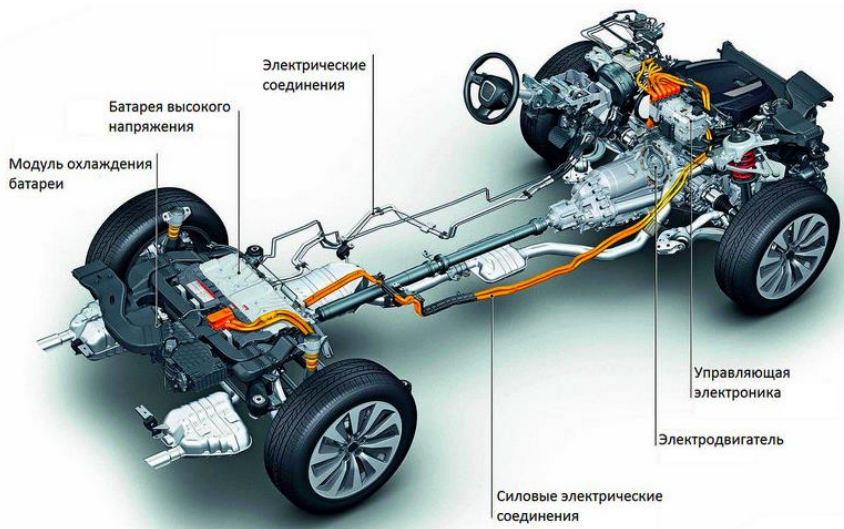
Устройство автомобиля с гибридным двигателем
